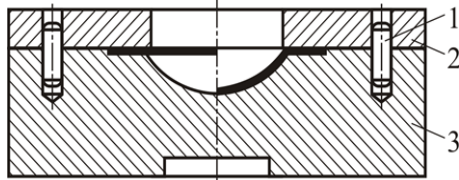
Конструктивна схема штампа для витягування, карбування та калібрування:
